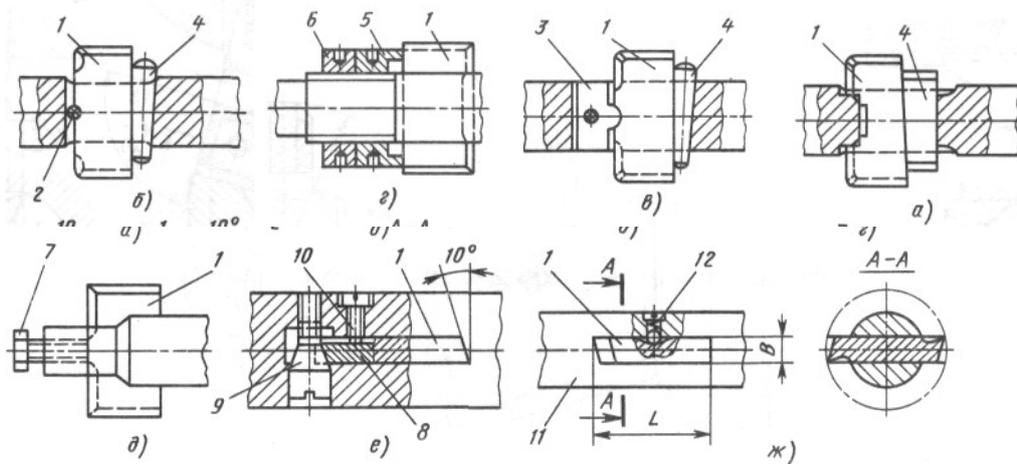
Основные типы крепления двусторонних пластинчатых резцов и блоков в оправках
